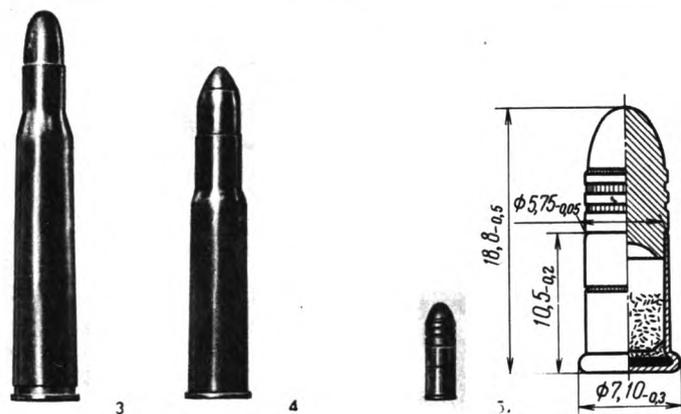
Патрон кольцевого воспламенения со свинцовой пулей и малокалиберным карабином и винтовкам калибра 5,6×16 мм: а) внешний вид патрона; б) схематический рисунок устройства патрона.
